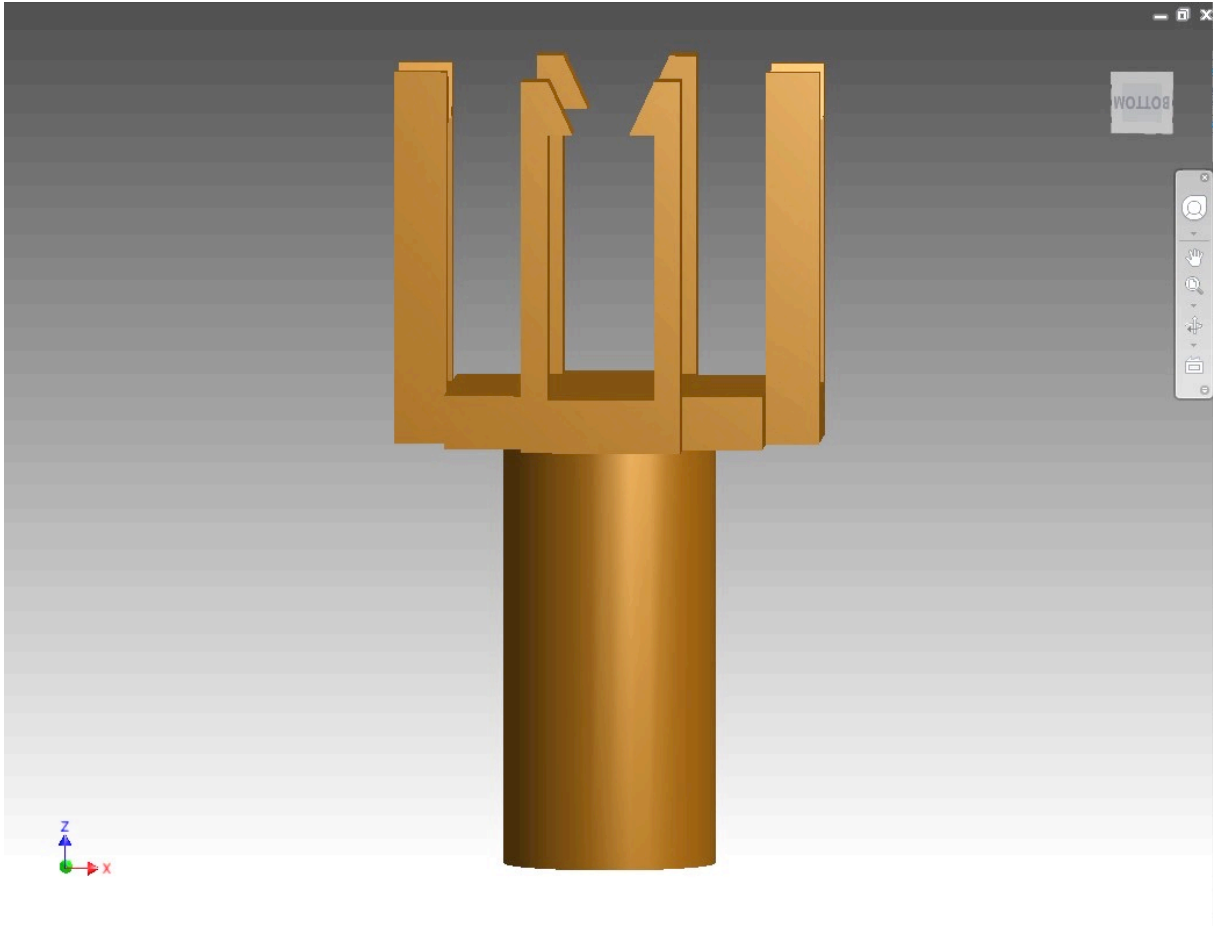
Pieza soporte entre motor e imanes diseñado en CAD
